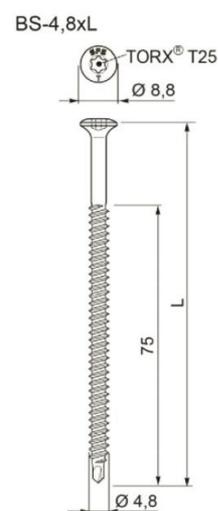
Vis SFS INTEC « IR2 4.8 » fastener + plaque de fixation IR 82x40
